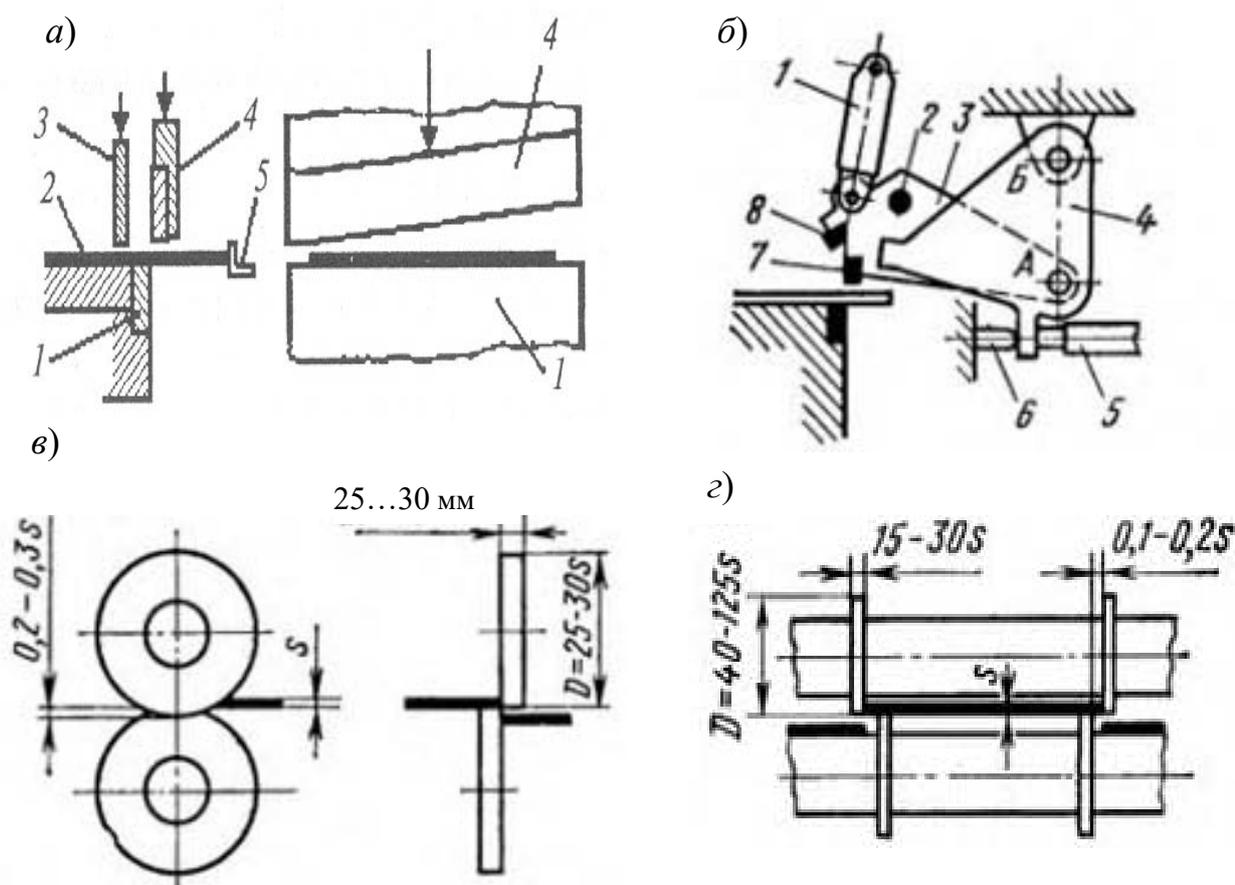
Схема резки металла на ножницах различных типов
